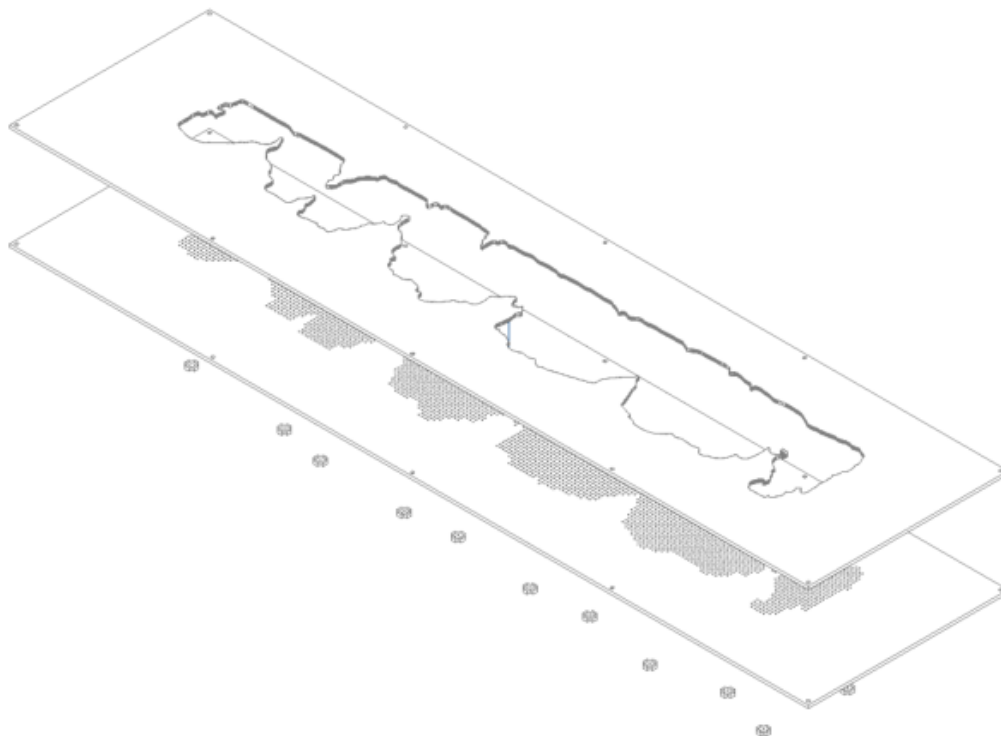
Vista de ensamblaje de la platina y la rejilla.
